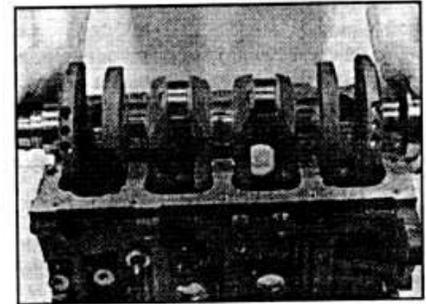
D.77. Установка коленчатого вала в блок цилиндров.
